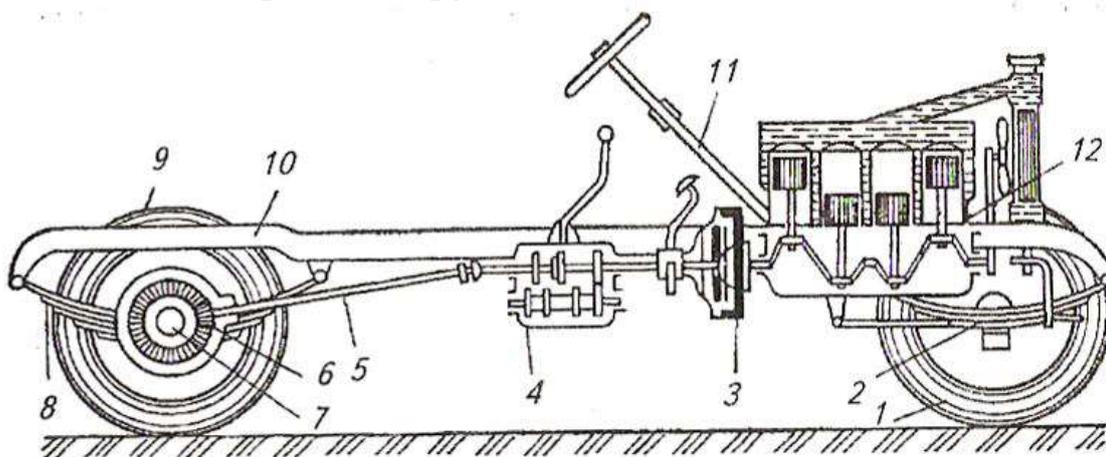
Расположение основных механизмов автомобиля: 1 – направляющее колесо; 2 – передняя подвеска; 3 – сцепление;
